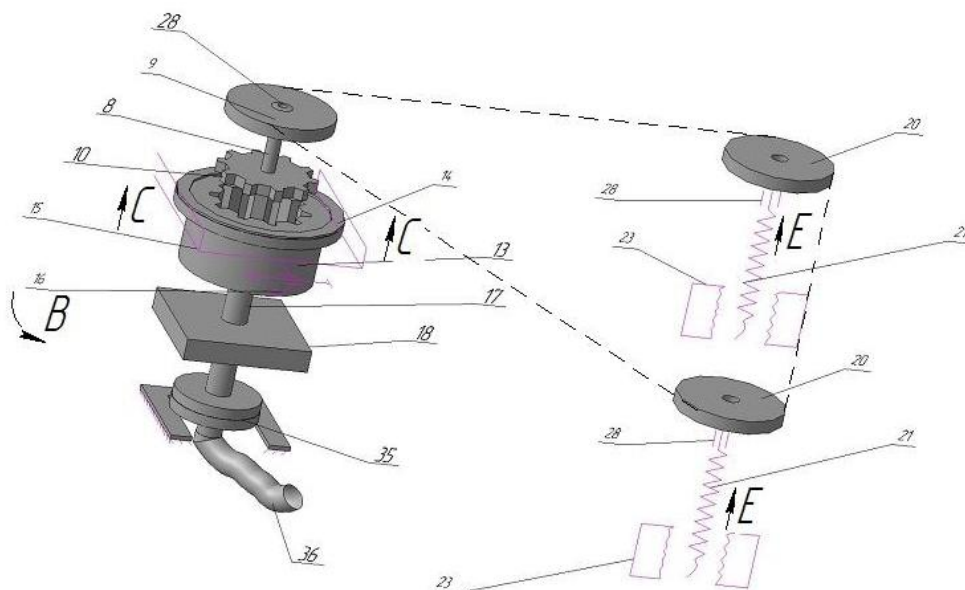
Кинематическая схема привода управления опорными стойками полуприцепа
